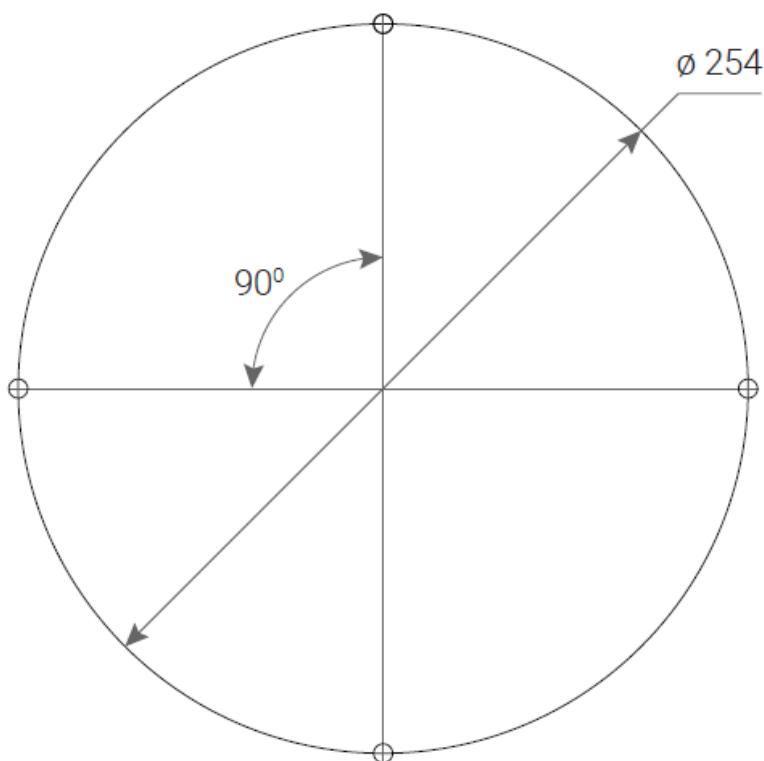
Схема разметки отверстий для монтажа манипулятора
